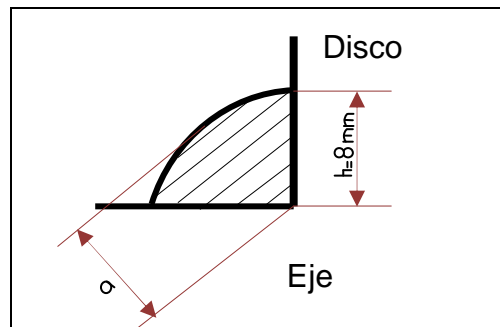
Soldadura de filete (eje y disco porta-martillos)
